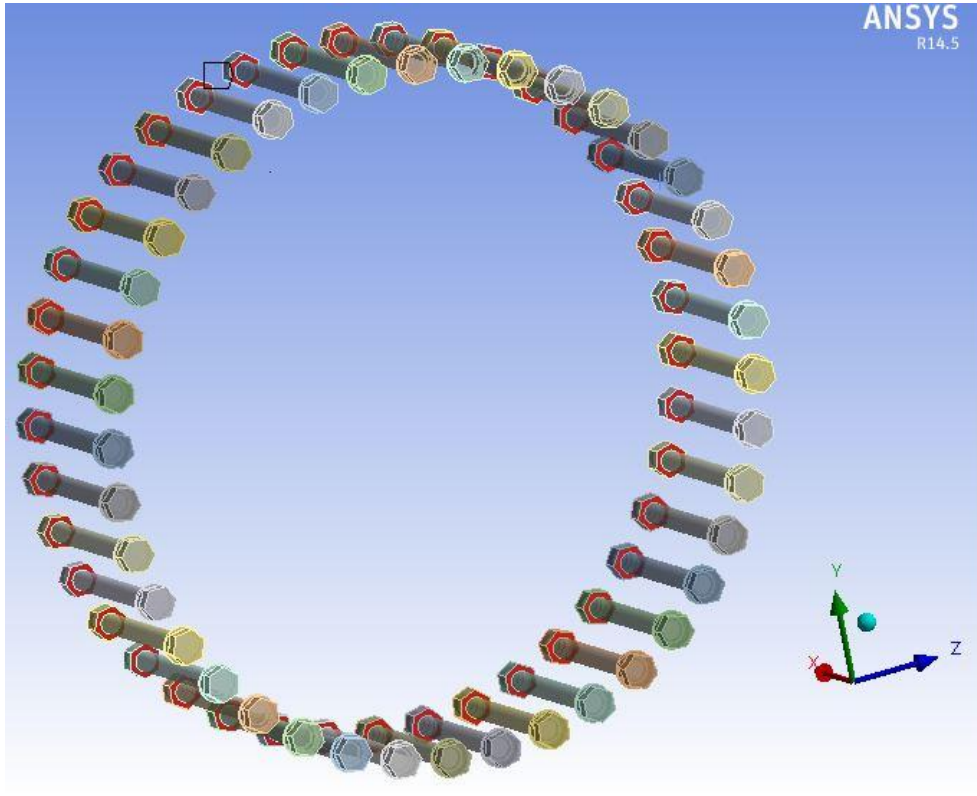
Ana şaft flanşı arası kontak bölgesi gösterimi.
